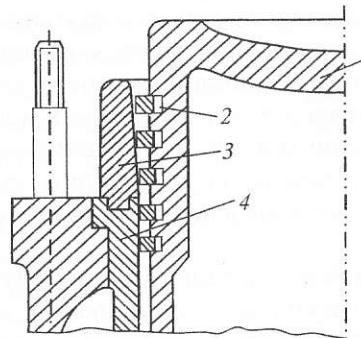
Пристрій для установлення поршня з поршневими кільцями в циліндр:
